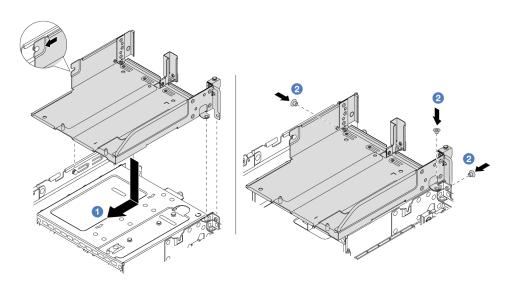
Установка лотка отсека для платы-адаптера Riser
